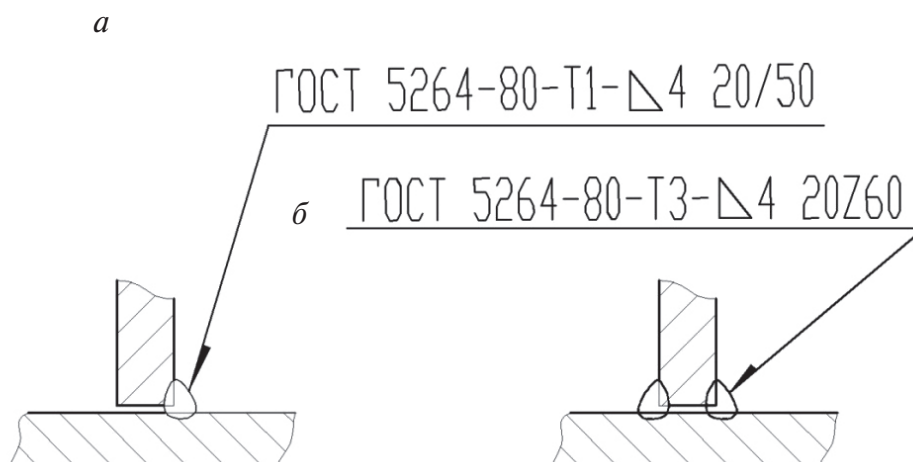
Примеры обозначения таврового сварного шва:
